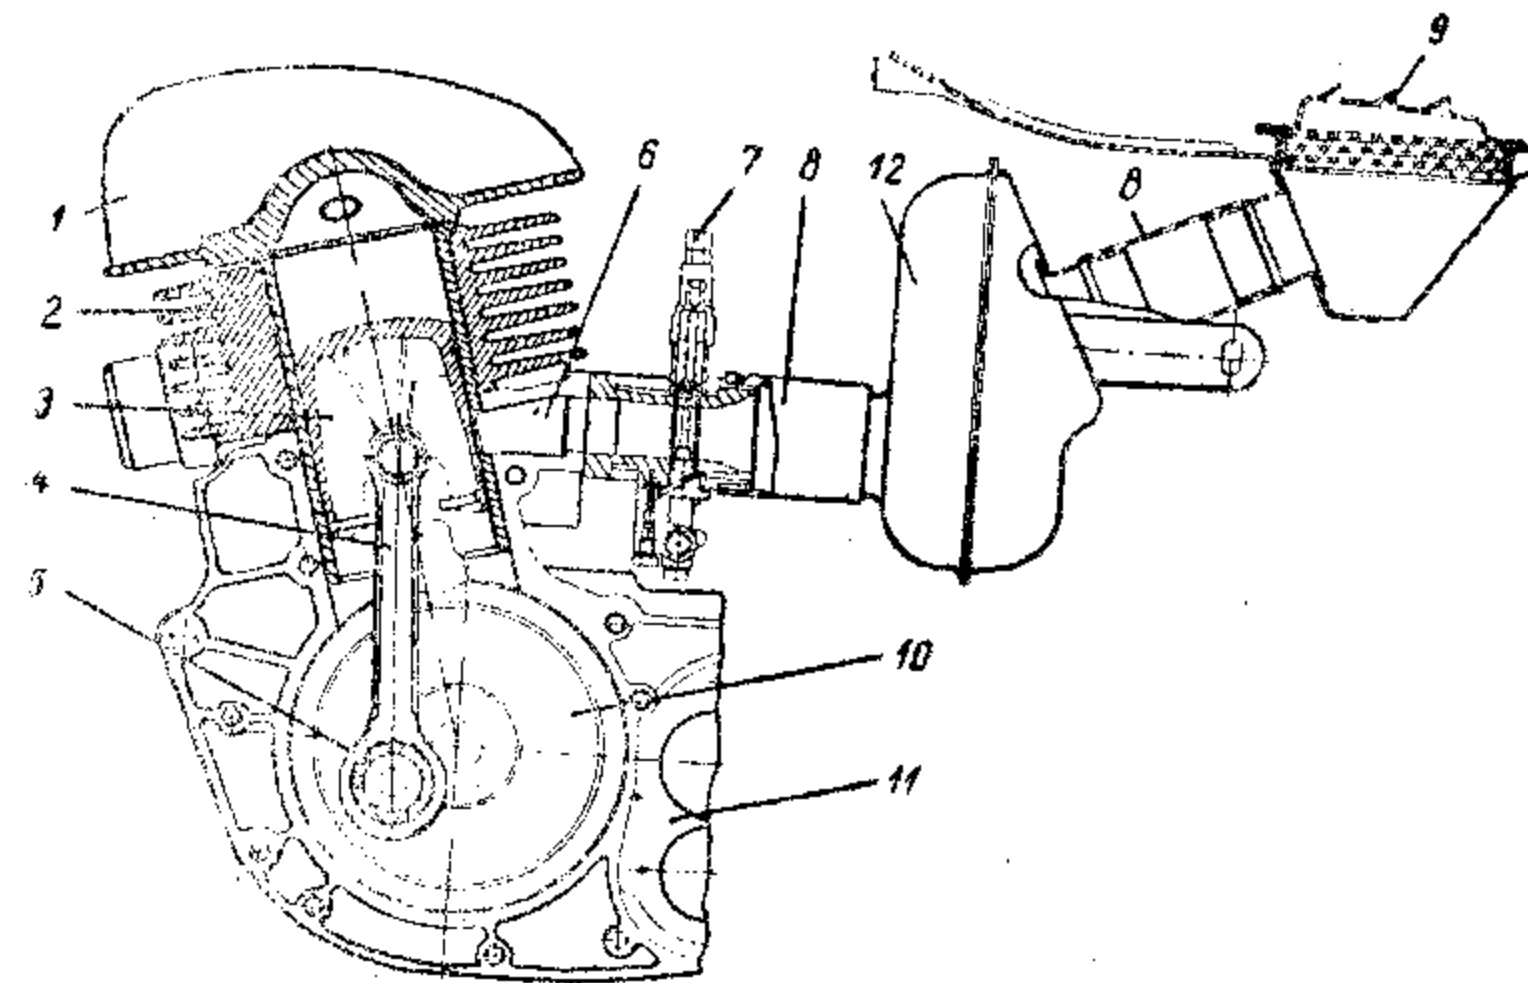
Продольный разрез двигателя (без крышки карбюратора).
